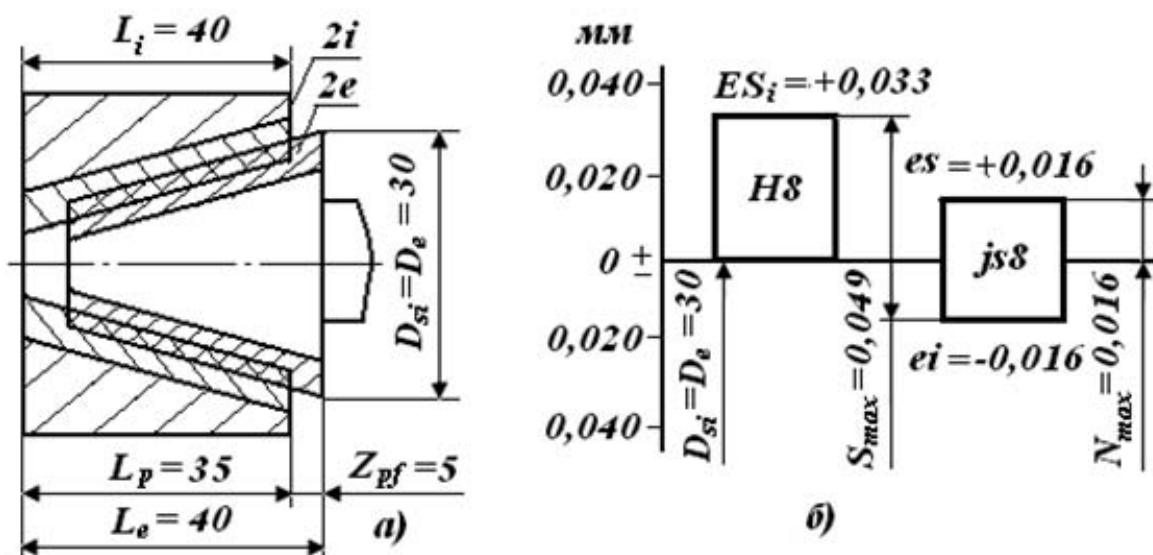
Ескіз з'єднання (а), поля допусків діаметра конусів корпусу і пробки (б)
